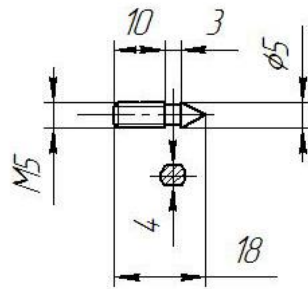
Креслення рисувалки слюсарного рейсмуса
